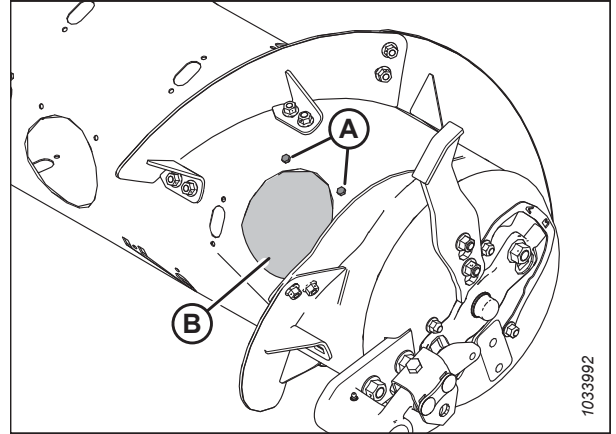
Tampas de acesso do sem fim - Lado direito
